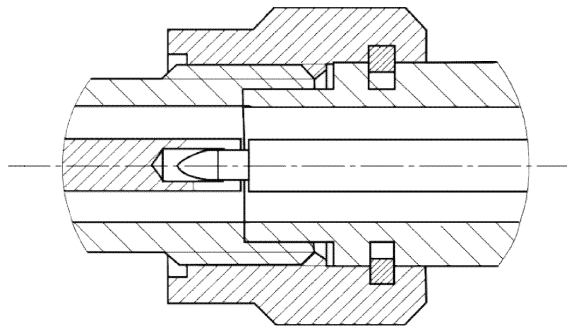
Соединители тип 3,5 мм и IX (розетка слева, вилка справа)
